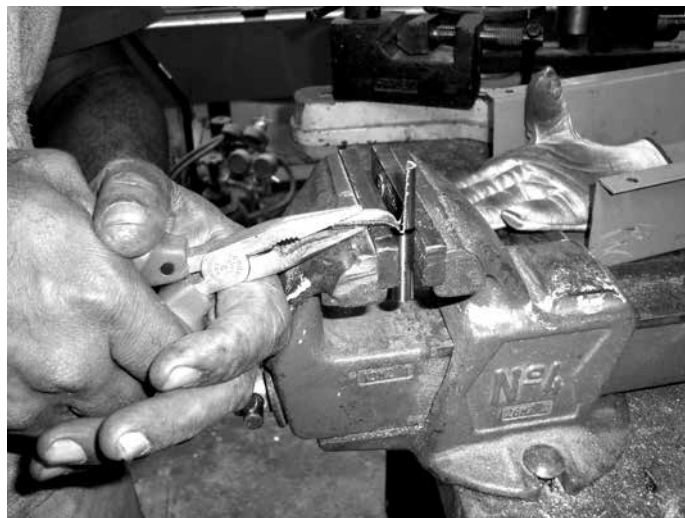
Técnico da Universidade FUMEC moldando os materiais para a montagem da máquina fiadora de PET.
